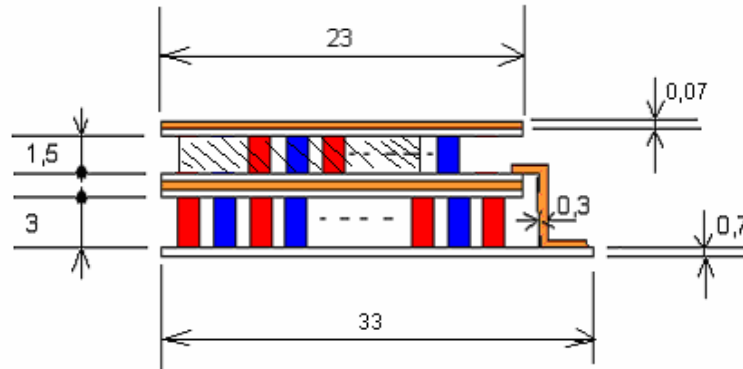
Dimensionado en mm del alzado lateral de TEG.
